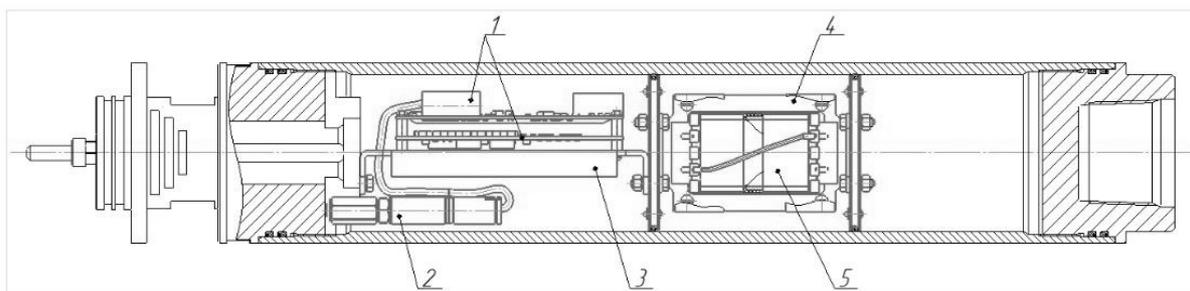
Компоновка ремонтного комплекта: 1- платы; 2-датчик давления; 3- несущая часть; 4-кранштайн; 5-дроссель
